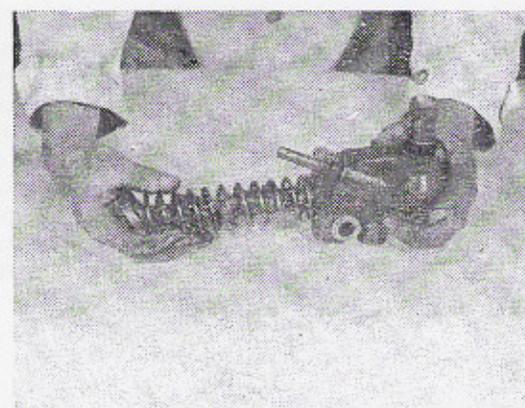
Remonter l'écrou du presse étoupe, le ressort
